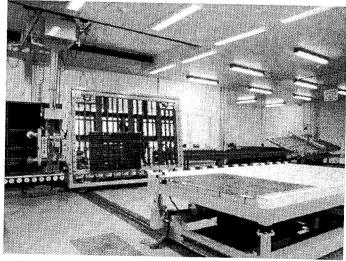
Produktionsanlagen für PV-Fassadenelemente bei Pilkington Solar International (Werkfoto)
